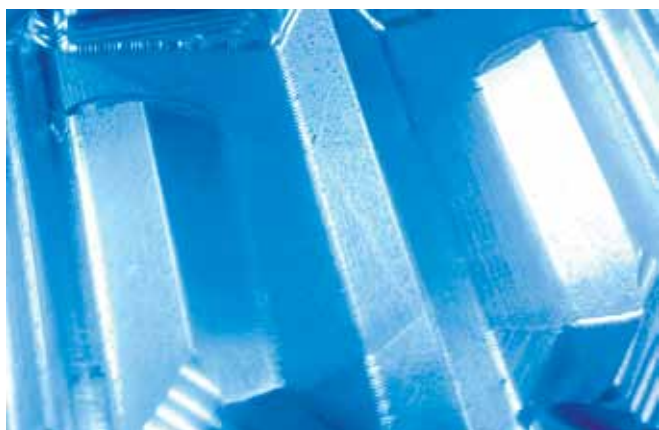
Рельефная поверхность, полученная фрезеровкой сферической фрезой с шагом 0,05 мм
